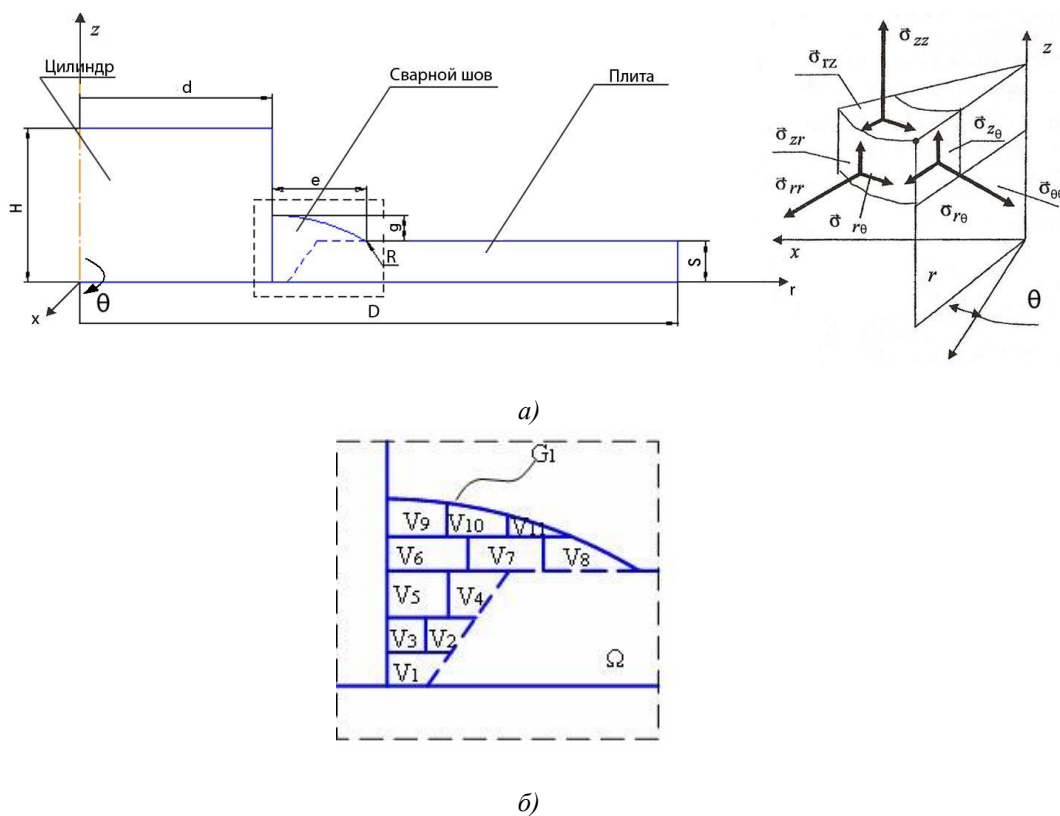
Схема сварного соединения(а) и схема очередности проходов(б)
